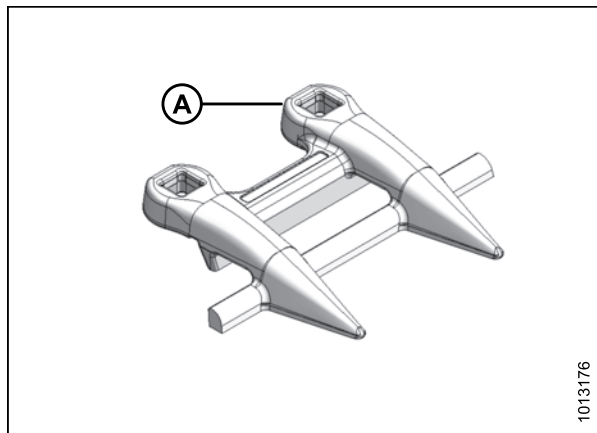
Центральный противорежущий палец: Двойной нож
